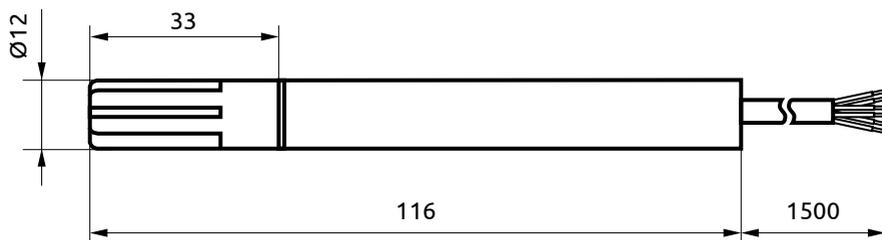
Габаритные размеры HTE.PF с кабелем
